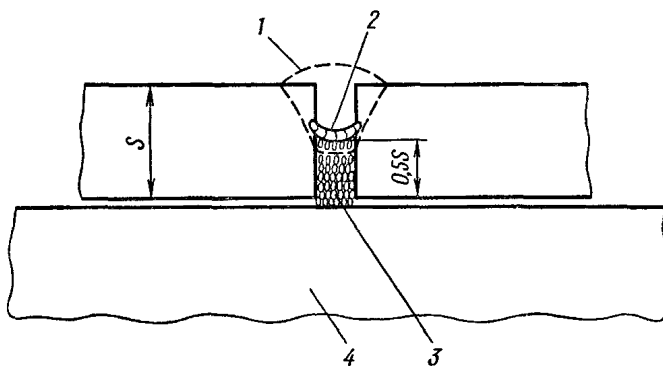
Схема постановки прихваток при сварке с применением металлохимической присадки:
